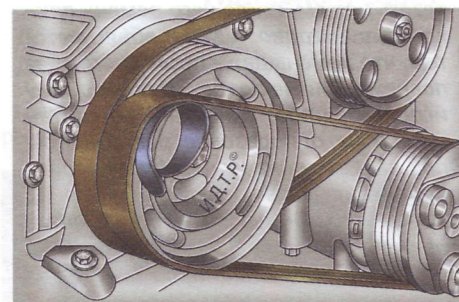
Монтаж ремня привода компрессора кондиционера на шкив коленчатого вала
